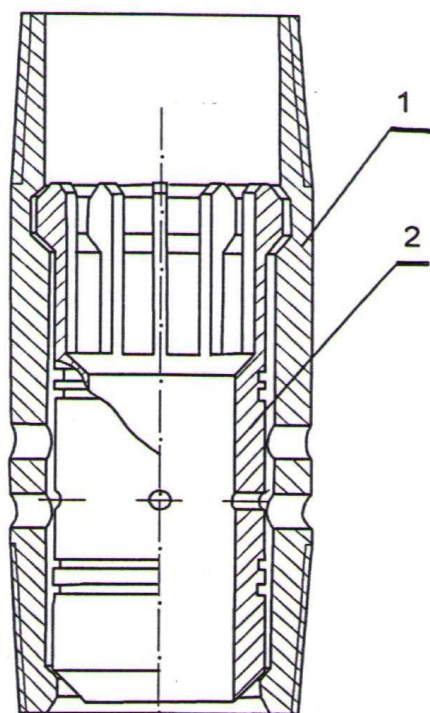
Перфорированный патрубок с забойным штуцером:
